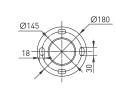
Чертеж и габаритные размеры фланца ОХОR-ОТ1-D108
